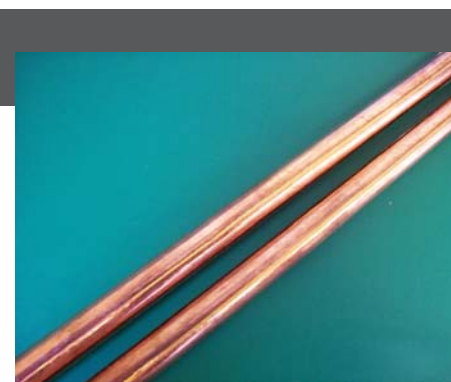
Tubes en cuivre de 10 mm soudés par laser
